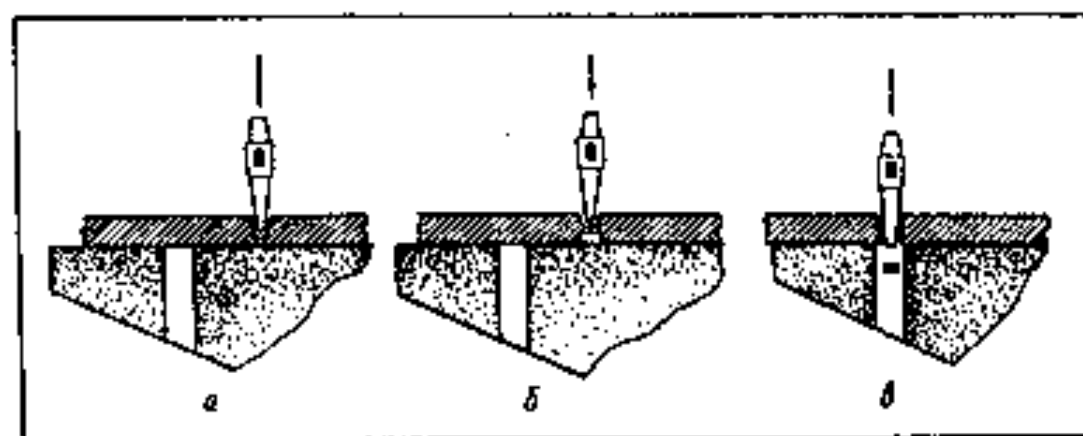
Пробивка с предварительным уплотнением металла (а, б, в — последовательность операций)
